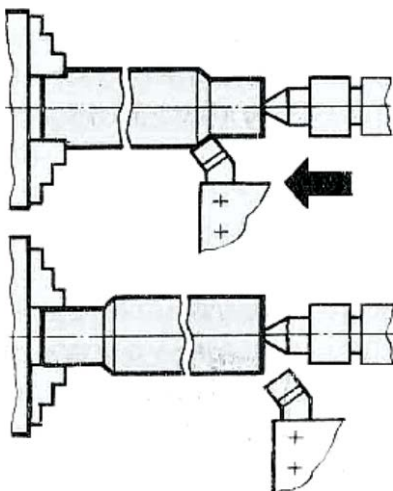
Обточування заготовок, закріплених в патроні з підтисканням заднім центром
